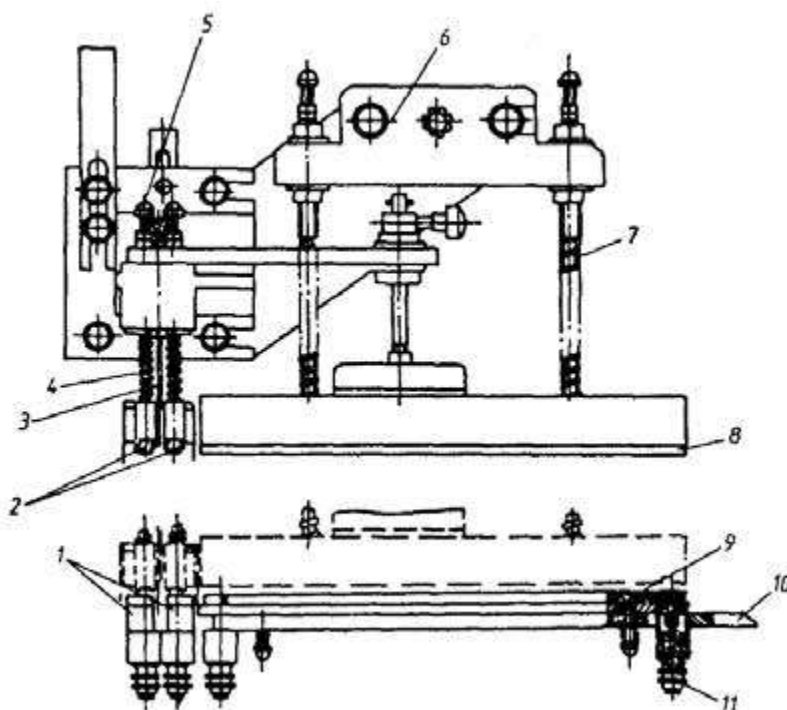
Пристрій для зварювання та різання напівавтомата А1-ФУБ: 1,9 – поперечні і поздовжні зварювальні губки; 2,8 – поперечні і поздовжні затискачі, 3 – ніж; 4,7 – пружини; 5 – тяги; 6 – траверса; 10 – верхня плита; 11 – клема
